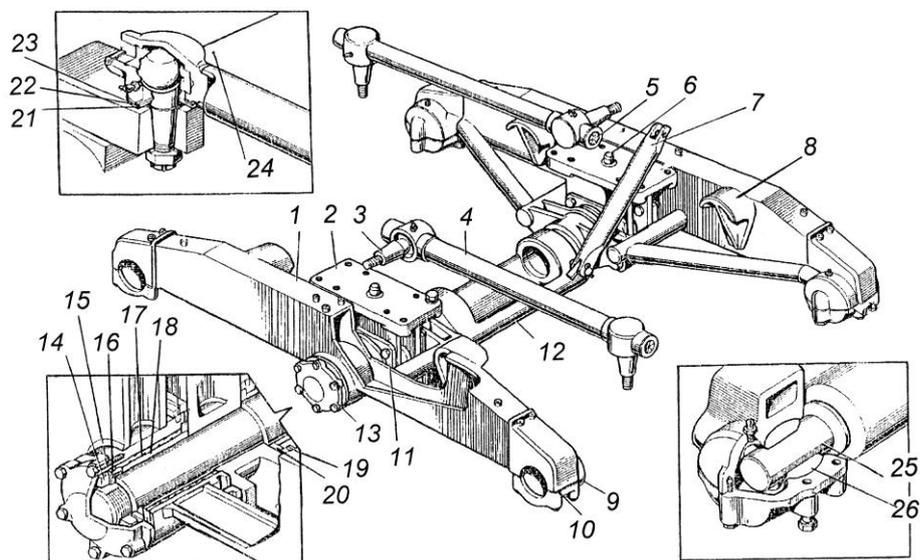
Подвеска задних мостов: 1 – балансир; 2 – кронштейн крепления балансира к стойке рамы автогрейдера; 3 – шаровой палец; 4 – реактивная штанга; 5 – регулировочная гайка; 6 – центрирующий штифт; 7 – распорная штанга; 8 – упор; 9 – крышка шаровой опоры балансира; 10 – регулировочные прокладки; 11 – корпус сальника; 12 – ось балансиров; 13 – крышка оси балансиров; 14 – гайка; 15 – стопорная шайба; 16 – упорная шайба с фиксатором; 17 – втулка; 18 – неподвижная втулка; 19 – уплотнитель; 20 – шайба; 21 – коническая пружина; 22 – прокладка; 23 – обойма; 24 – задний мост; 25 – установочный палец заднего моста; 26 – шаровая опора
